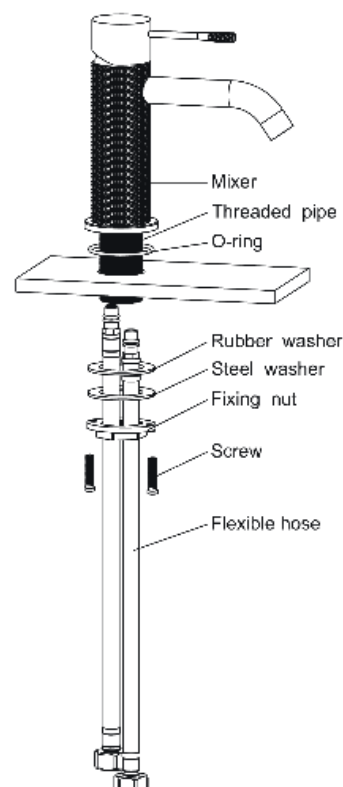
° Fig. 1 — Aufbau ° assembly
